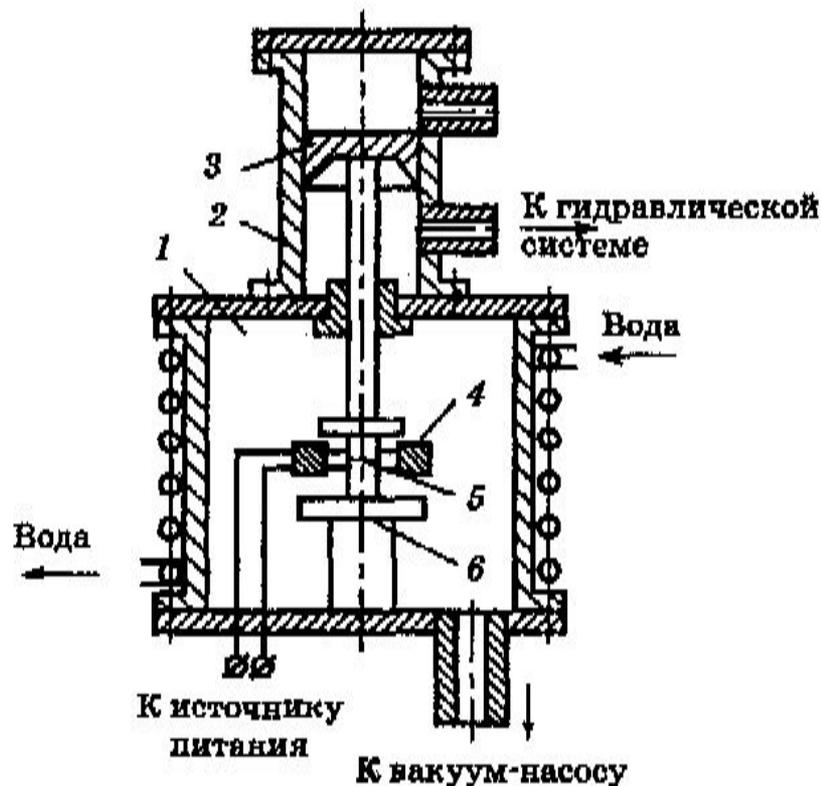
Принципиальная схема установки для диффузионной сварки в вакууме:
